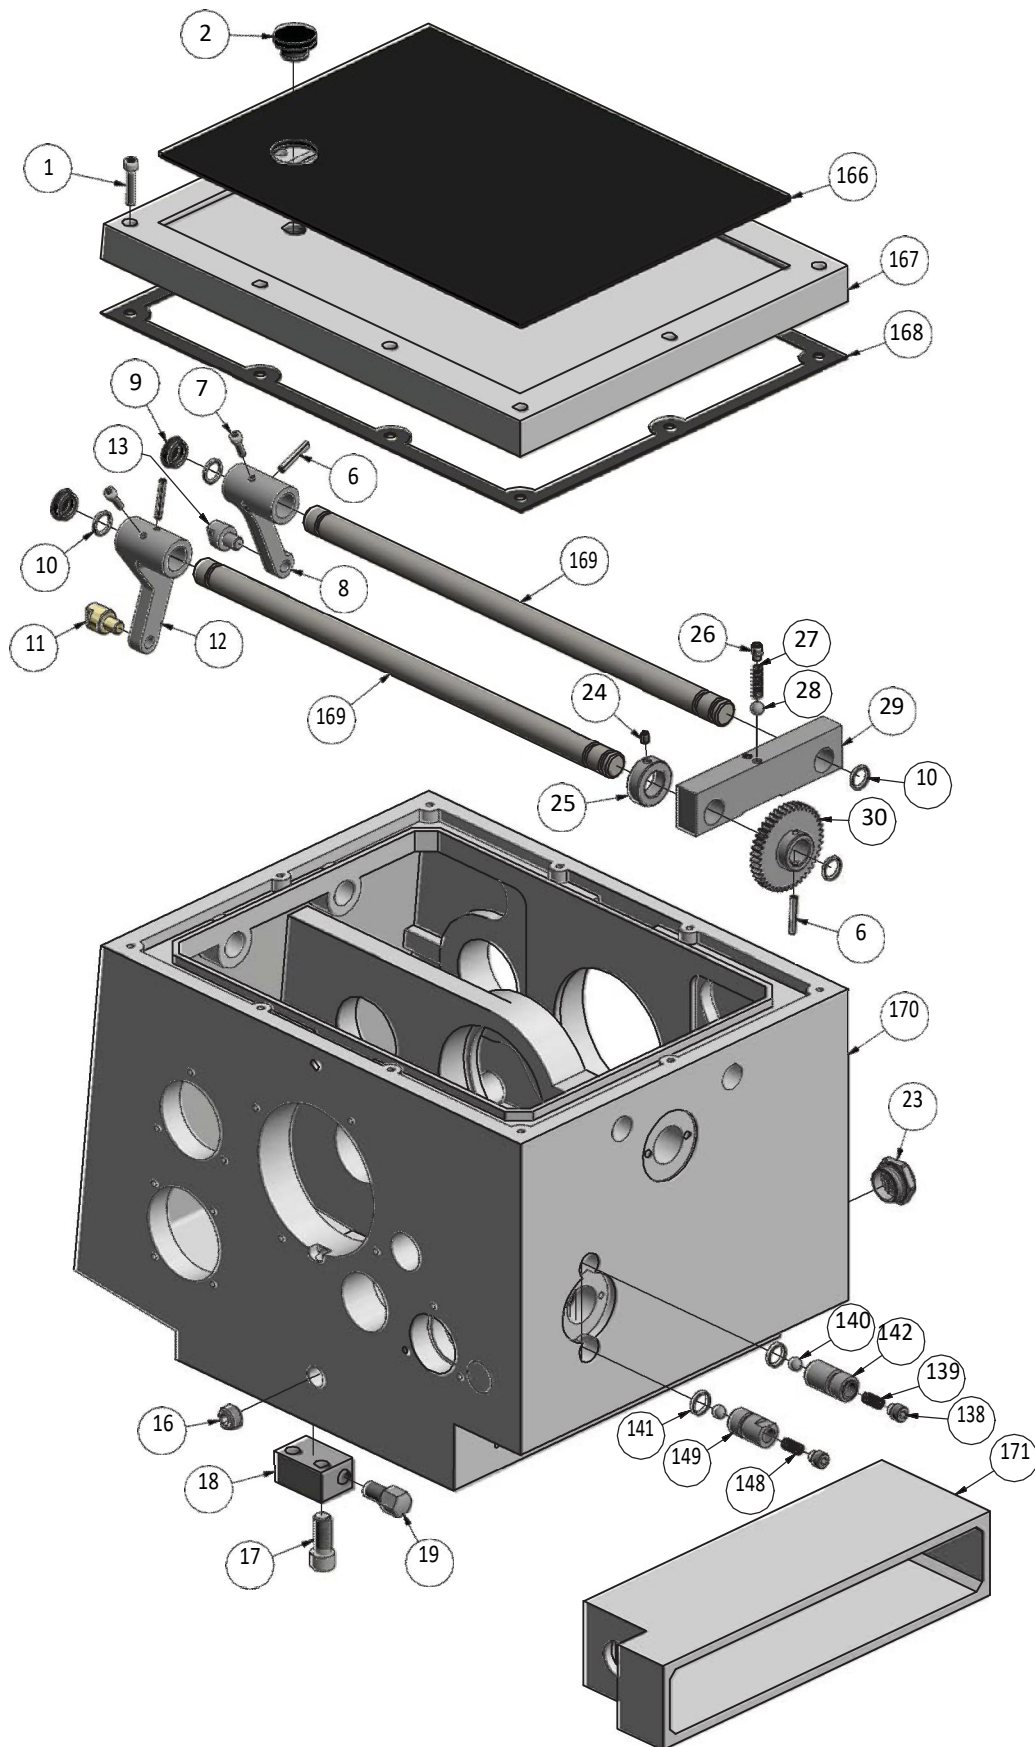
Spindelstock 2-9 - Cabezal 2-9
